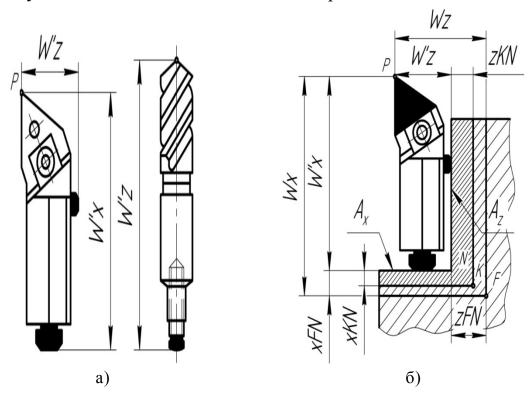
Схемы, поясняющие наладку режущего инструмента на станках: а – инструмент с регулировочными элементами; б – схема установки резца в гнезде суппорта
